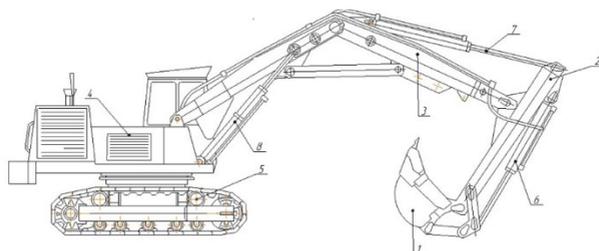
Экскаватор ЭО-4121: 1 – ковш; 2 – рукоять; 3 – стрела; 4 – базовый трактор; 5 – гусеничная тележка; 6 – гидроцилиндр управления ковшом; 7 – гидроцилиндр управления рукоятью; 8 – гидроцилиндр управления стрелой.
